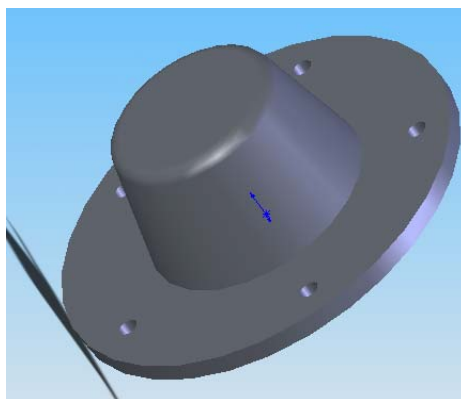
Базовая конструкция ступицы сошника сеялки СПУ-6
